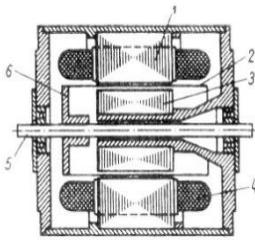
Асинхронный двигатель с полым немагнитным ротором: 1 — внешний статор; 2 — стакан ротора; 3 — внутренний статор; 4 — обмотка статора; 5 — вал; 6 — втулка крепления стакана ротора
